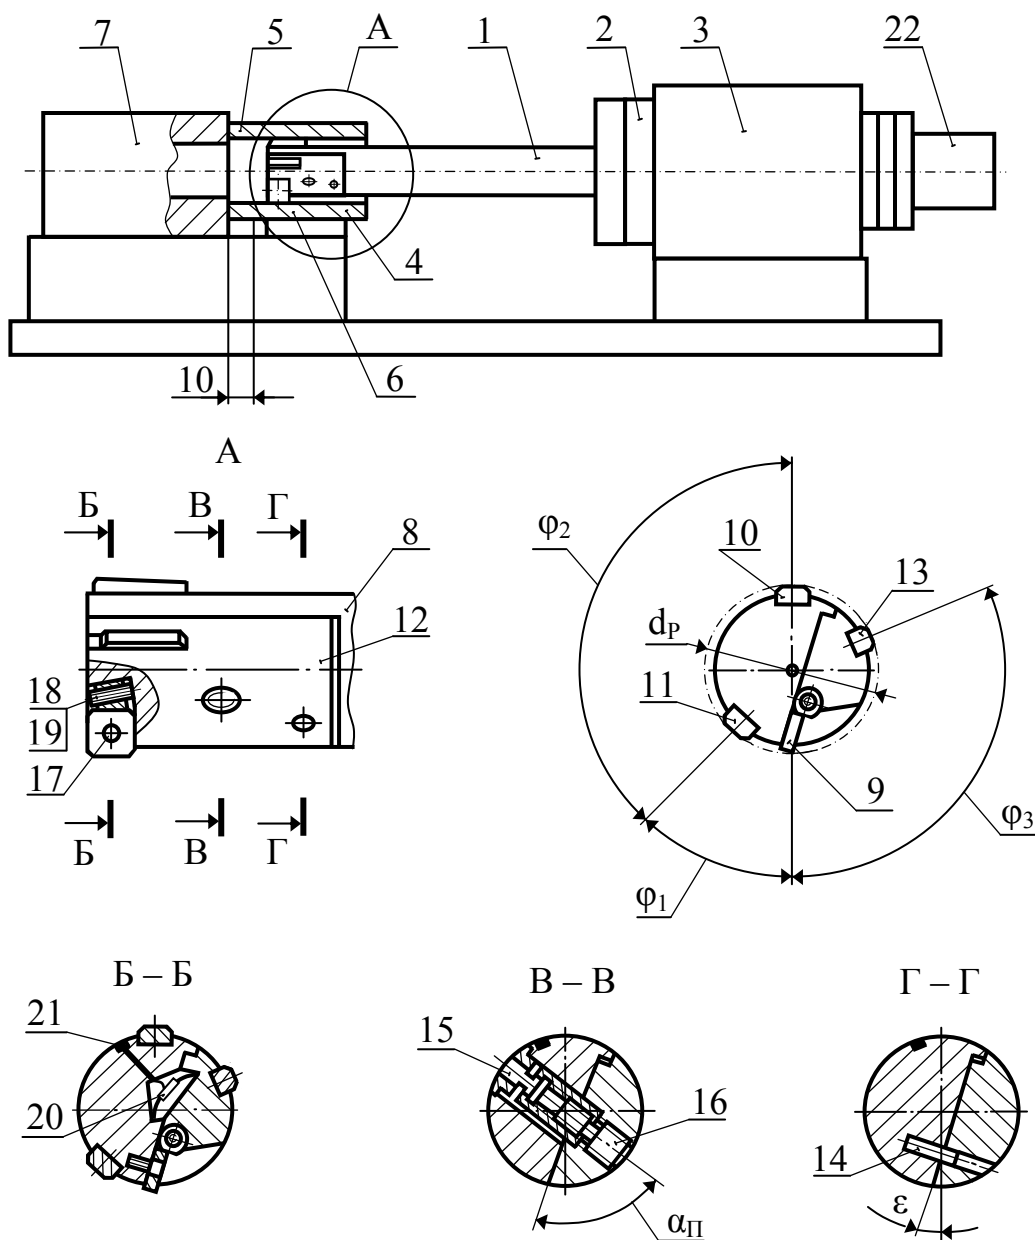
Схема устройства для автоматического контроля предельного размерного износа режущего и направляющих элементов расточного инструмента, а также направляющего участка отверстия кондукторной втулки и размерной точности обработки.
